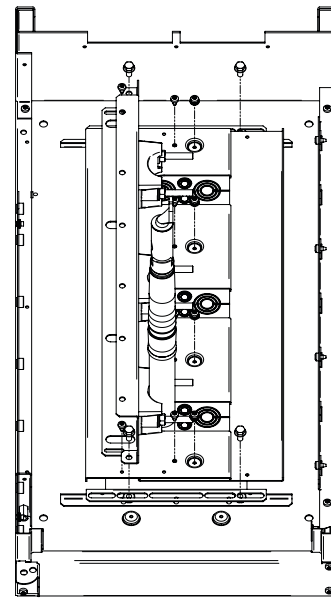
Instalación de las chapas del pavimento, de los listones guía cables, de los sujeta-cables y de los pasacables
